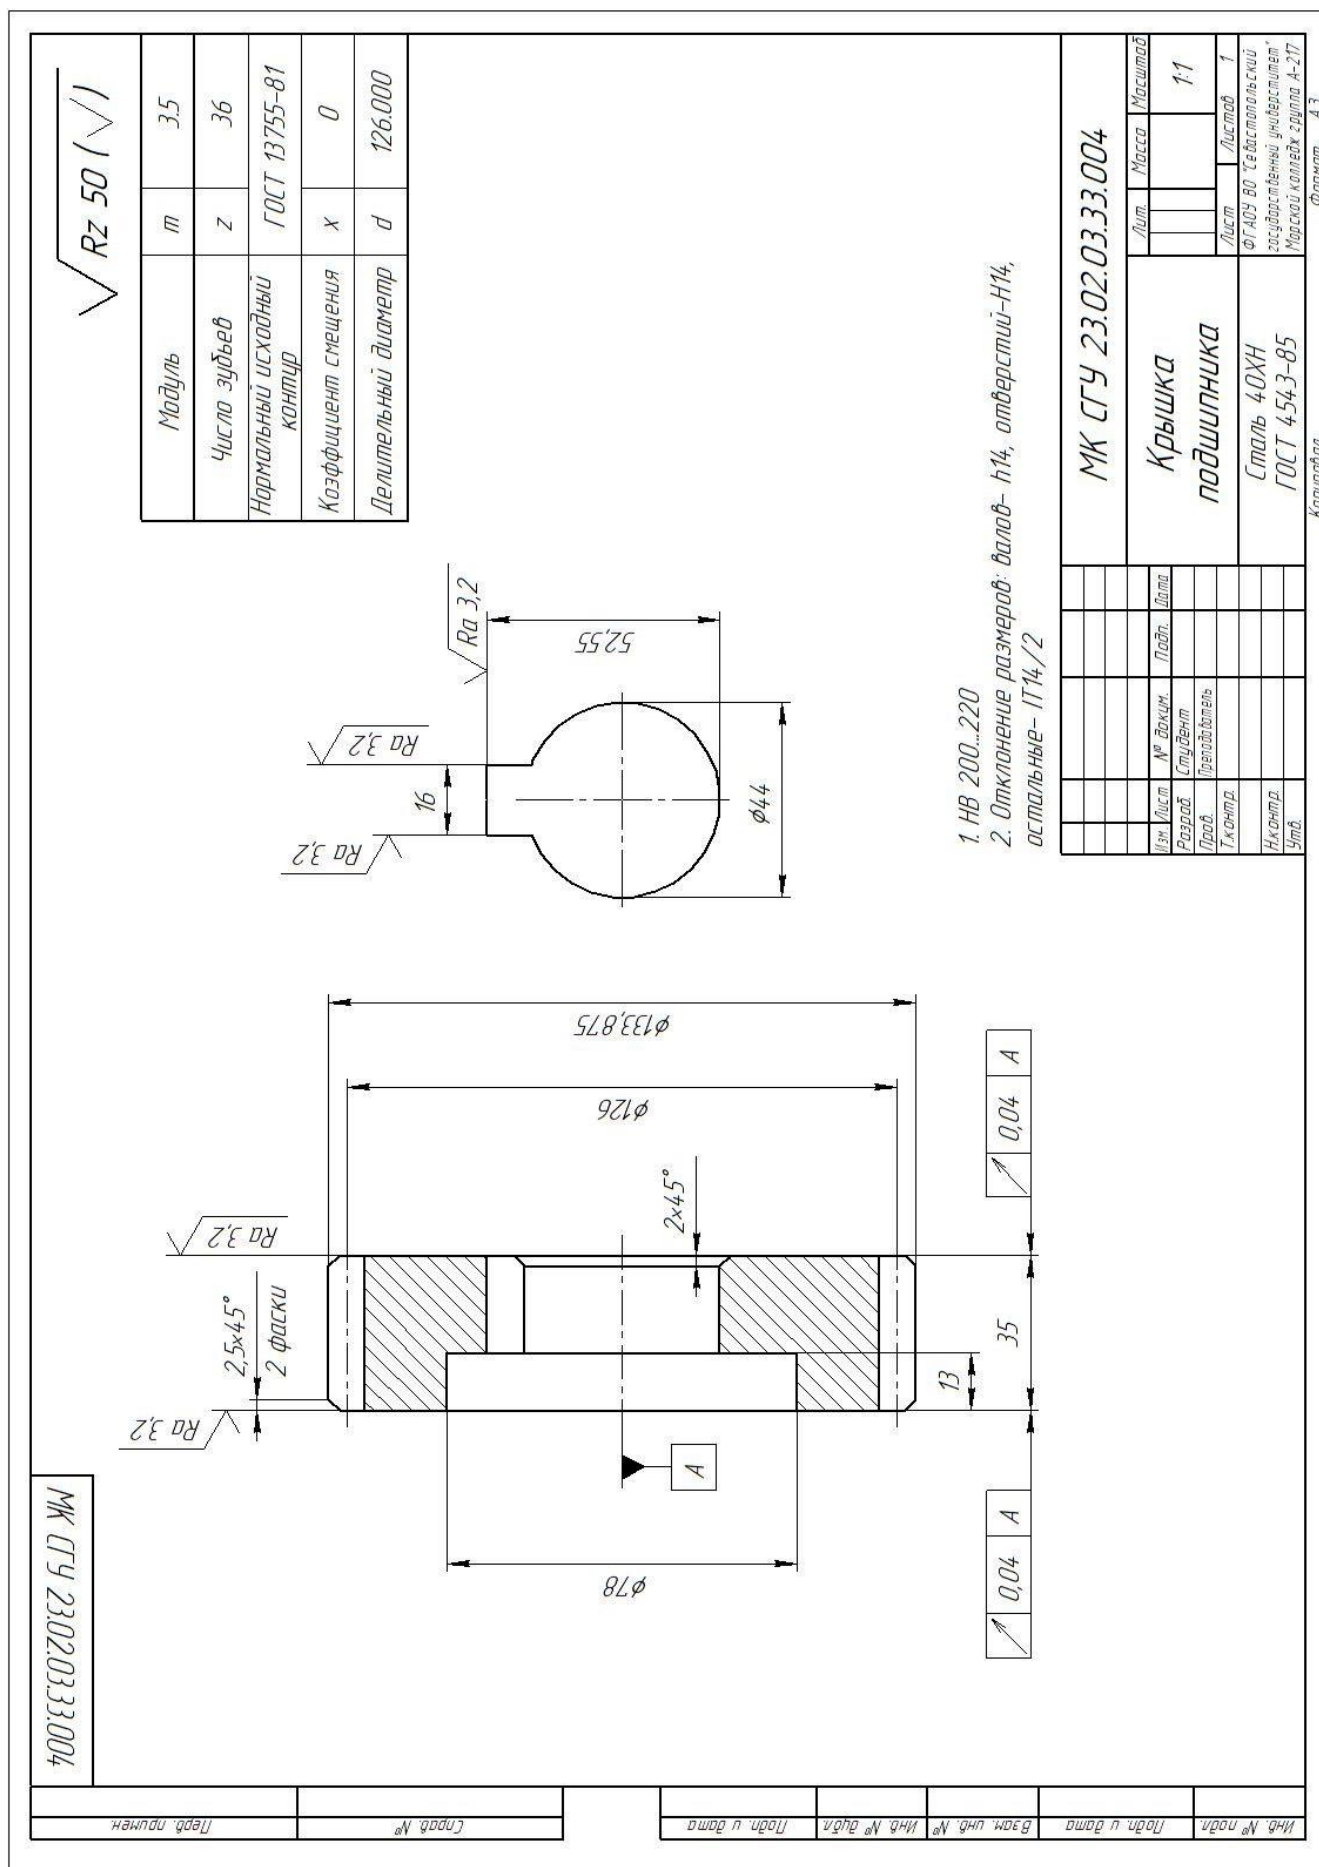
Пример выполненного чертежа детали колесо зубчатое
